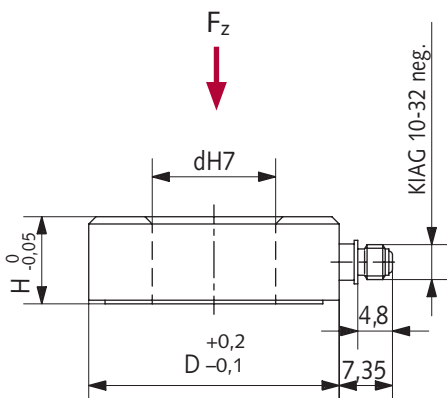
Dimensions rondelle de charge, Type 9001A ... 9031A
